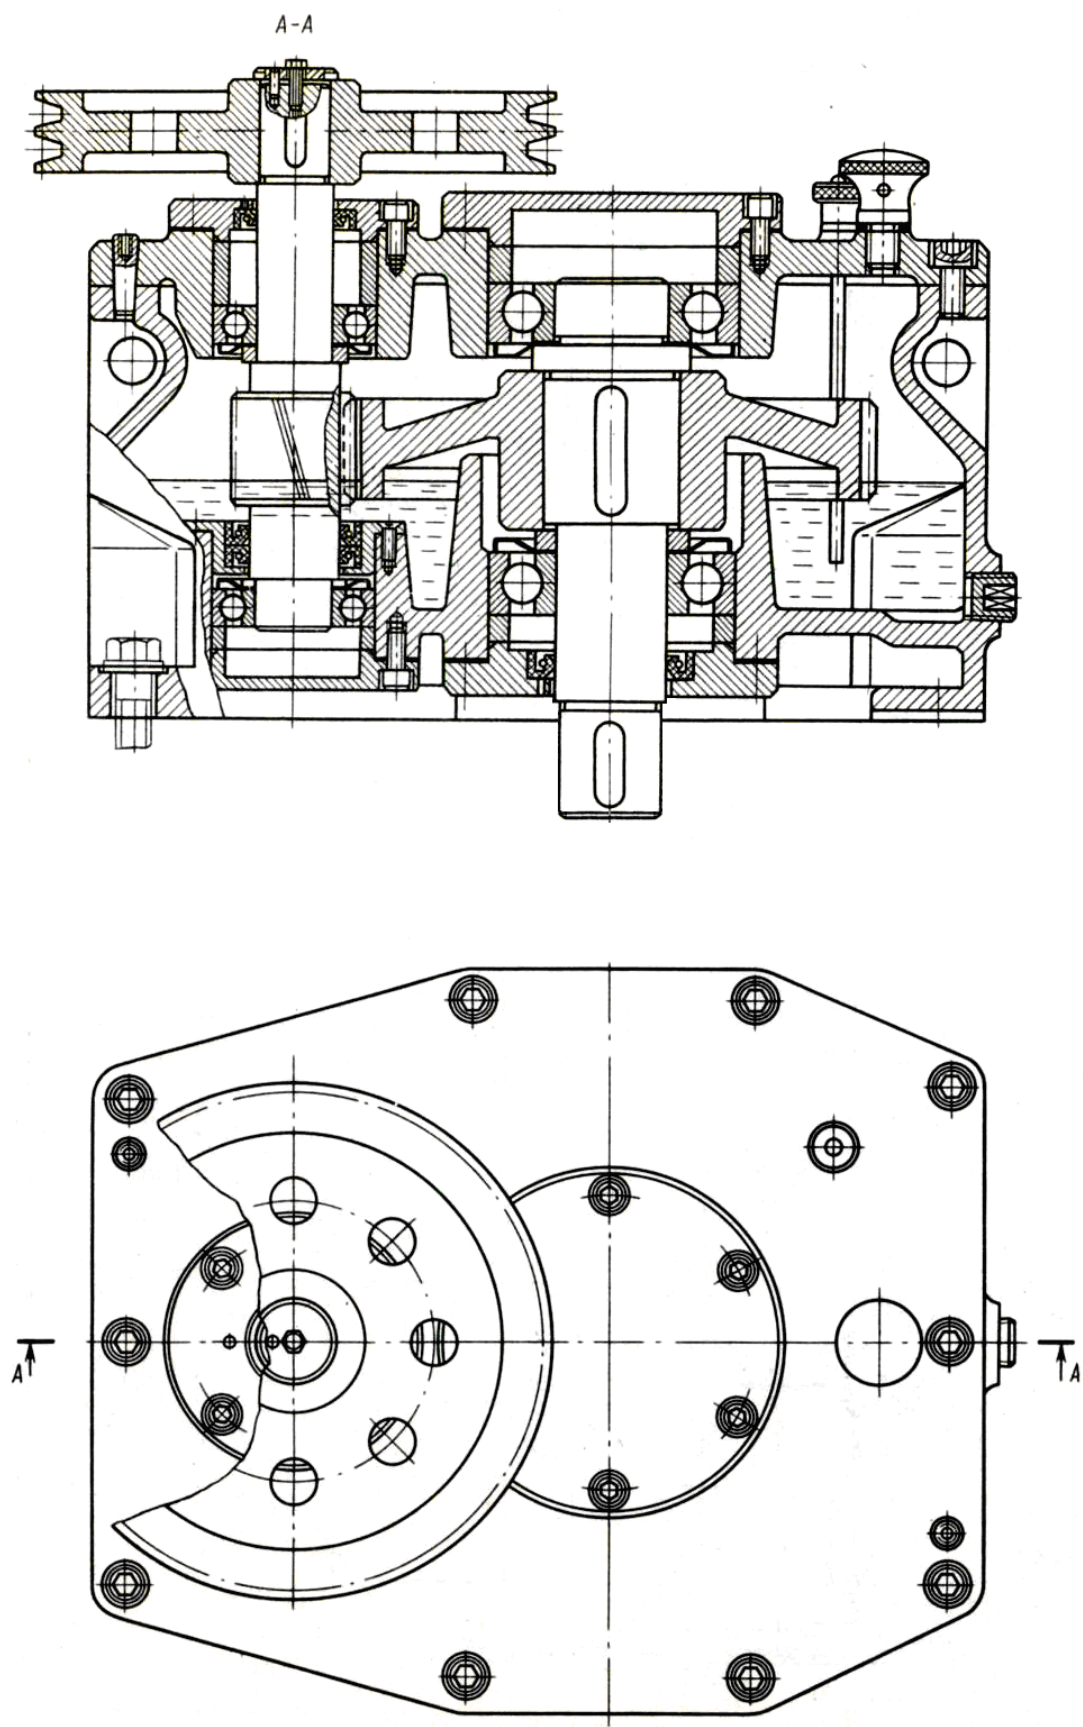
Редуктор цилиндрический с вертикальными валами
